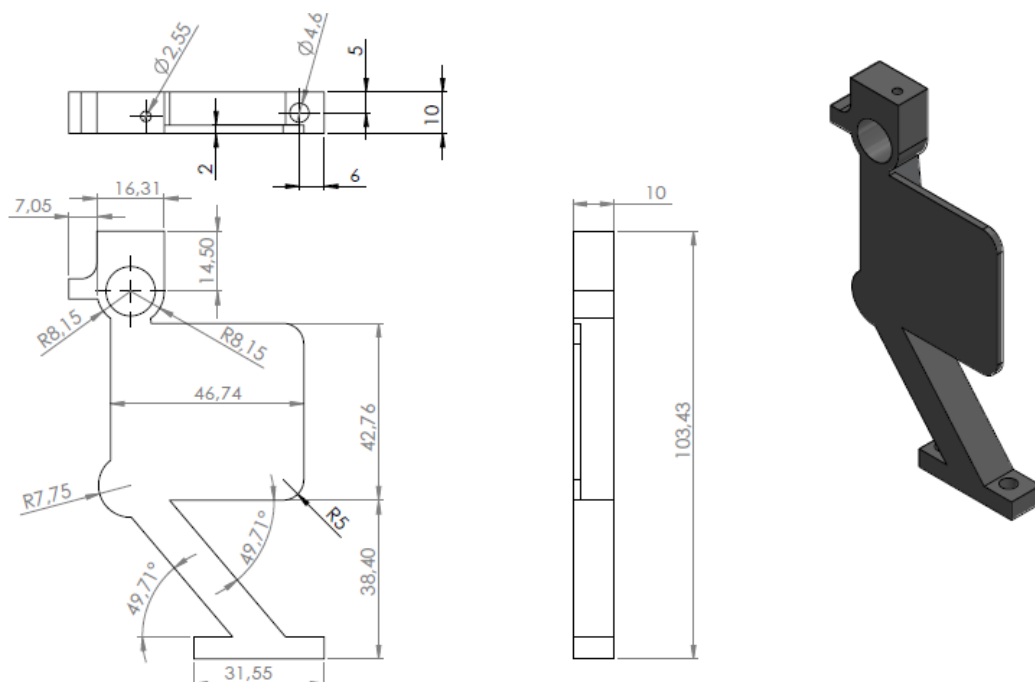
3D модель крепления баз гексакоптера в SolidWorks
